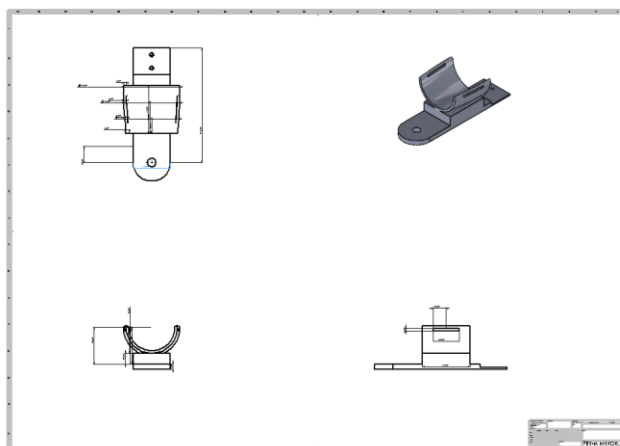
Perspectiva isométrica y vistas diédricas de la pieza 6.
